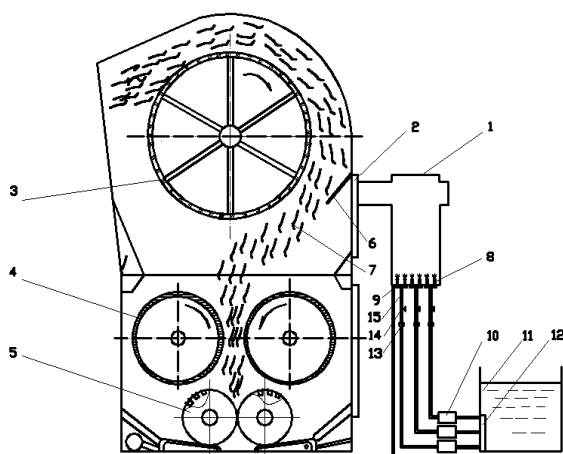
Схематичный общий вид конденсора с портативным увлажнителем волокна.
